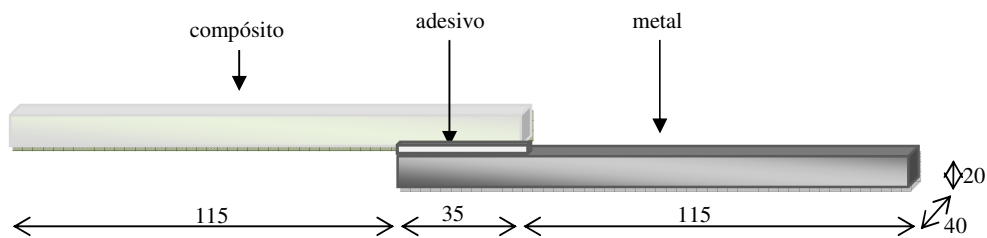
Esquema representativo das dimensões (mm) de uma junta colada em sobreposição simples de um material compósito com um metal.
